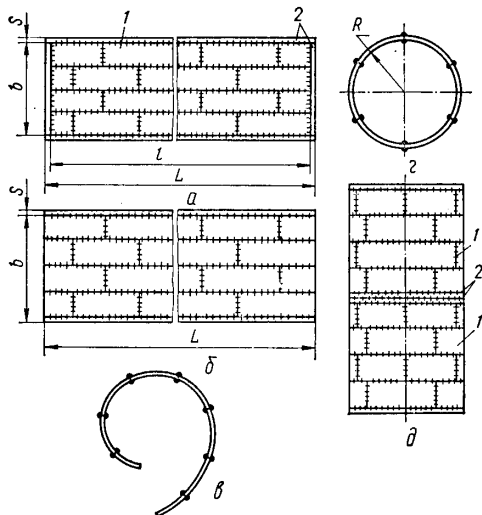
Схема изготовления резервуара из углеродистой стали с переходными полосками из высоколегированной стали:
